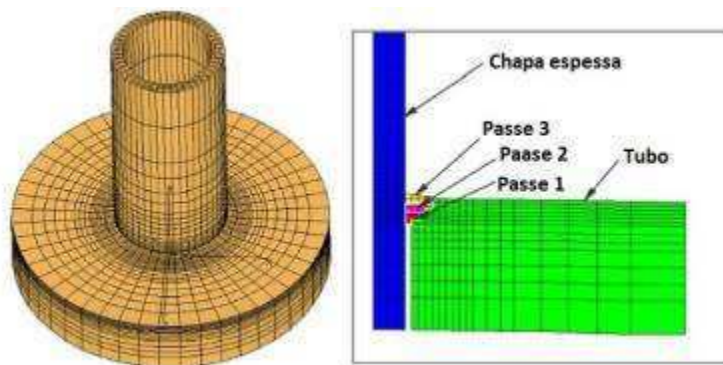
Componente de tubulação e passe de soldagem (Adaptado DENG, 2013).
